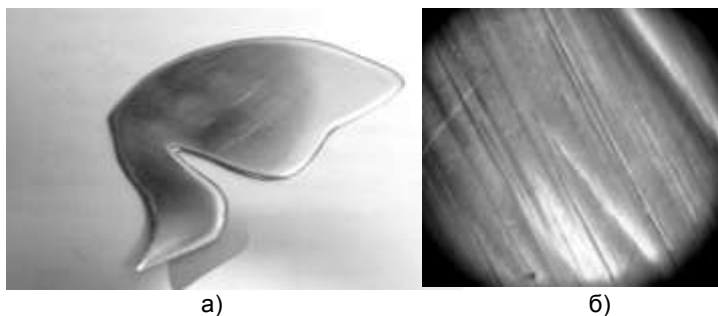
Деталь «крыло» после чистовой шлифовки: а) внешний вид детали; б) фрагмент детали под микроскопом (ув.×1000)
